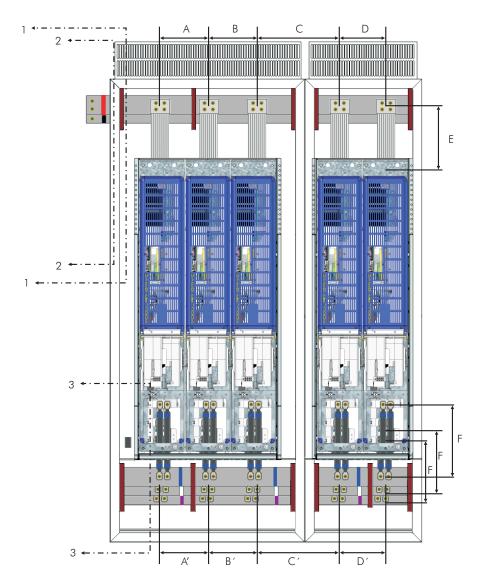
Detalles de la simetría constructiva (Layout) del armario (tablero)
